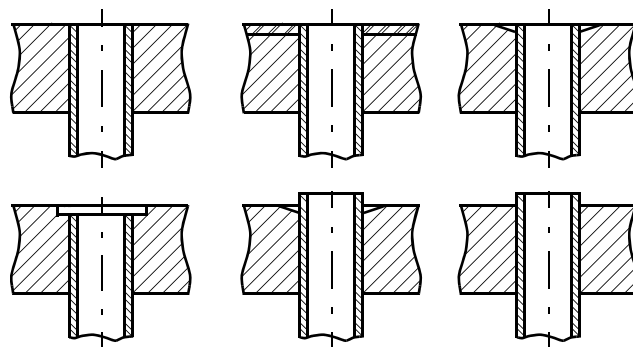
Типовые виды сварных соединений "труба — трубная доска"
